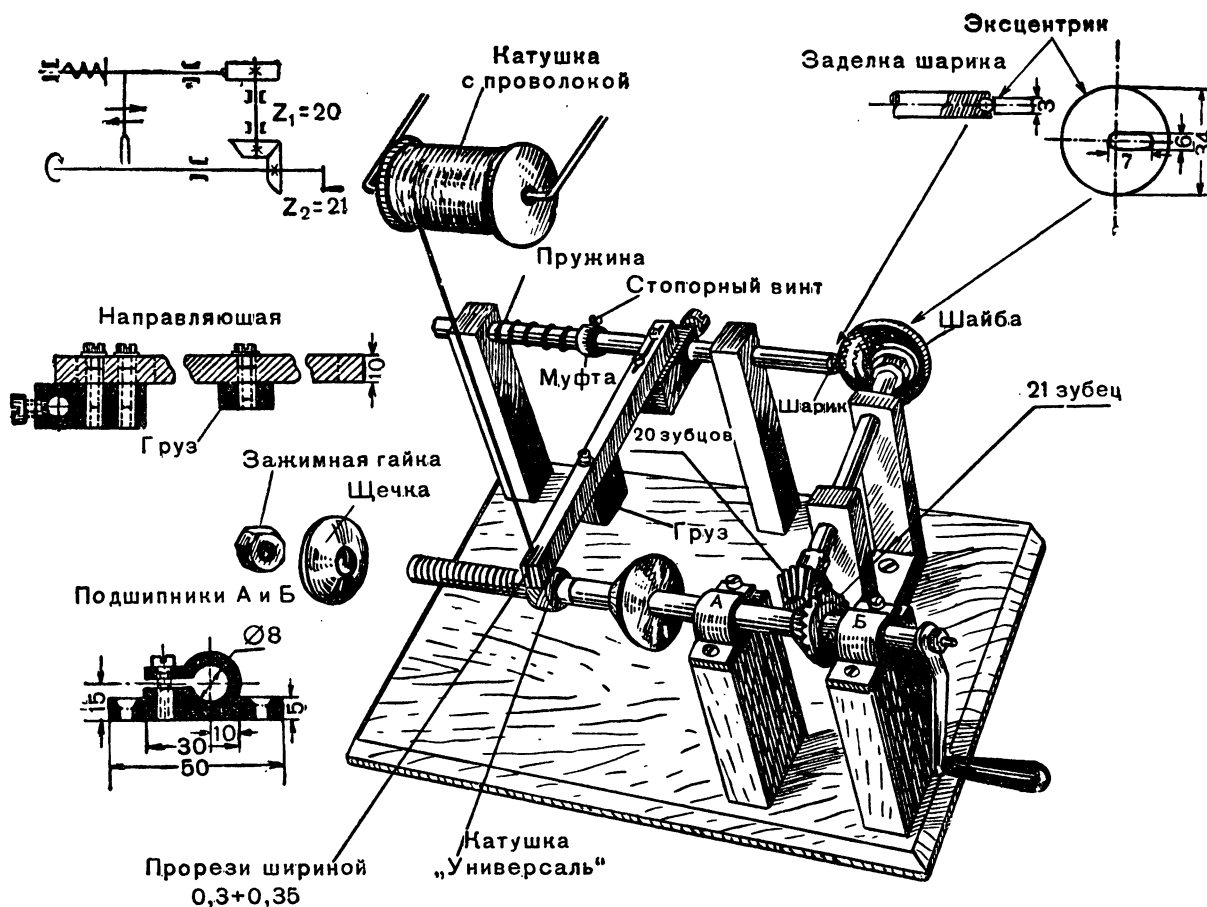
Приспособление для намотки катушек типа «Универсаль».
